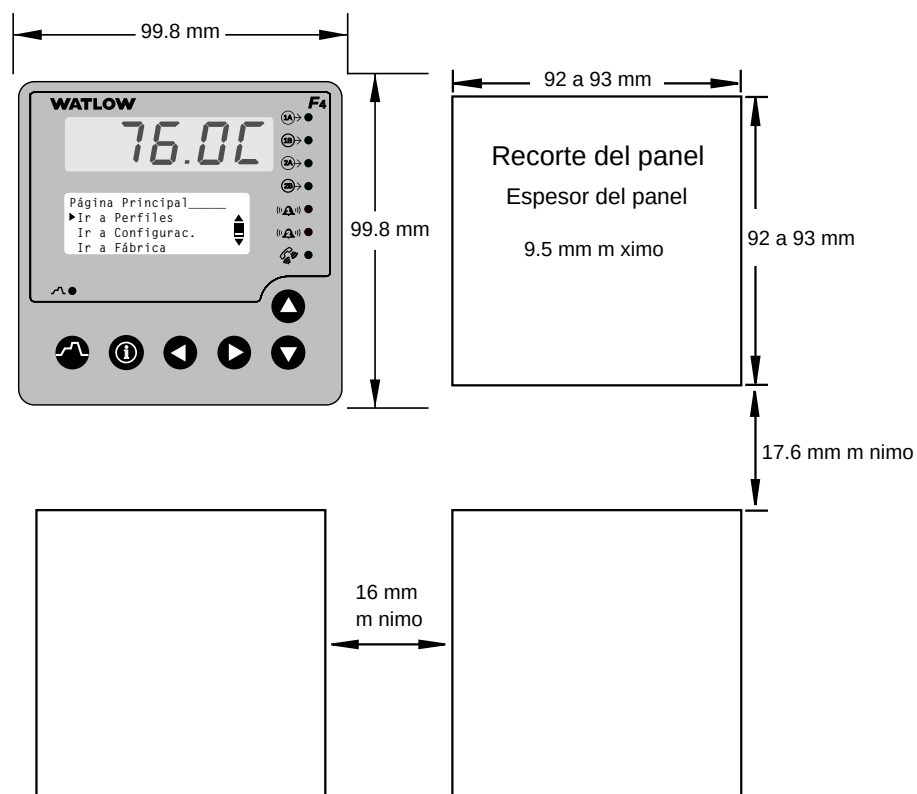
Dimensiones de recortes múltiples del panel.
